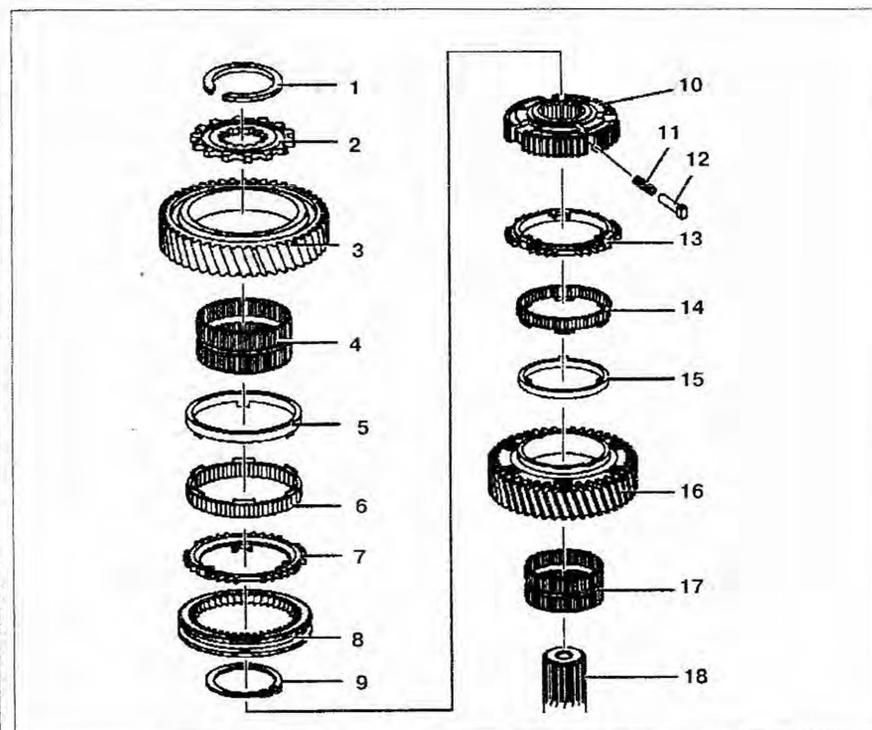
Снятие и установка шестерни 2-й передачи:
